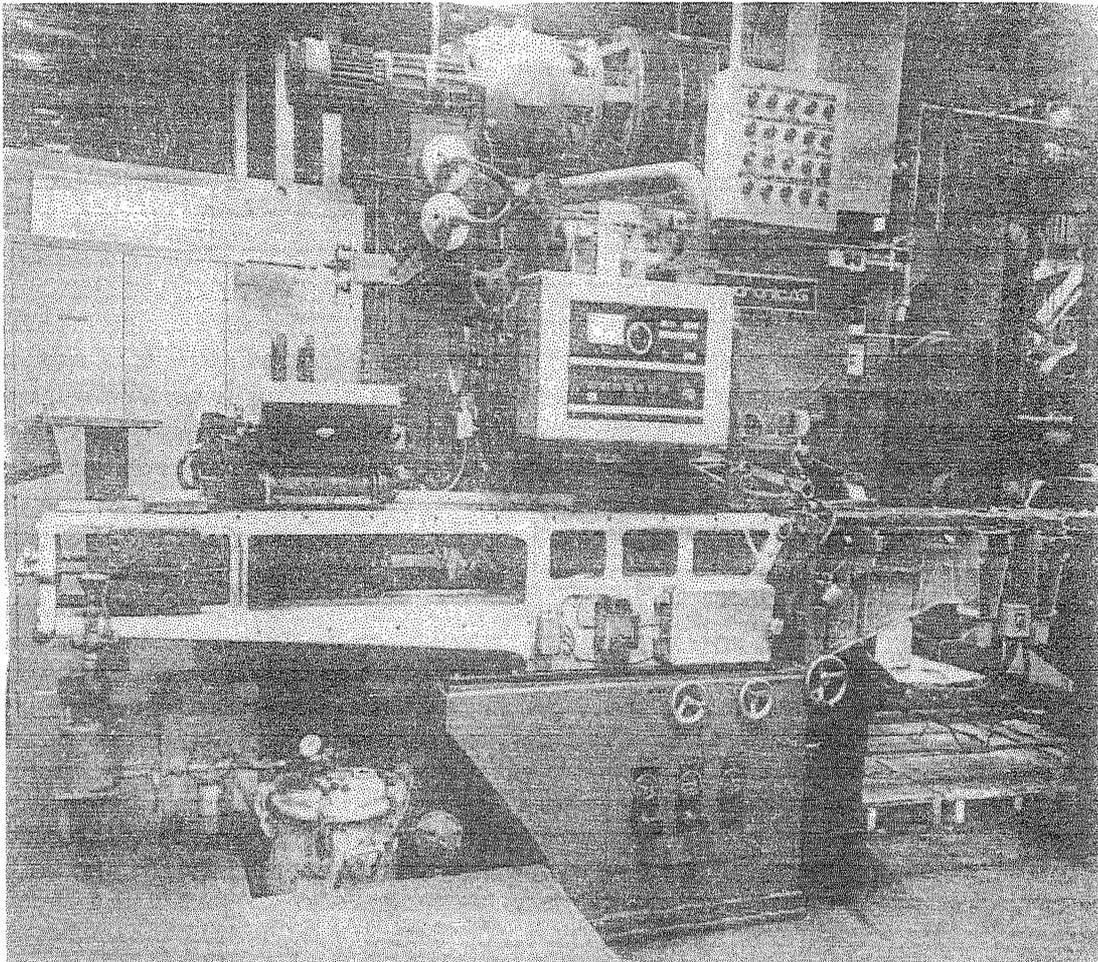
a Vista Frontal de la soldadora.
